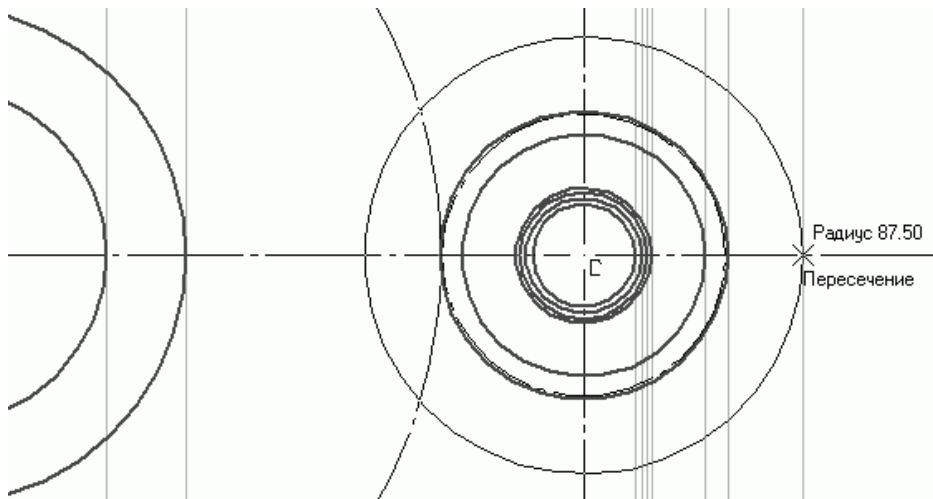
Процесс построения крышек подшипников и выходного конца ведущего вала
